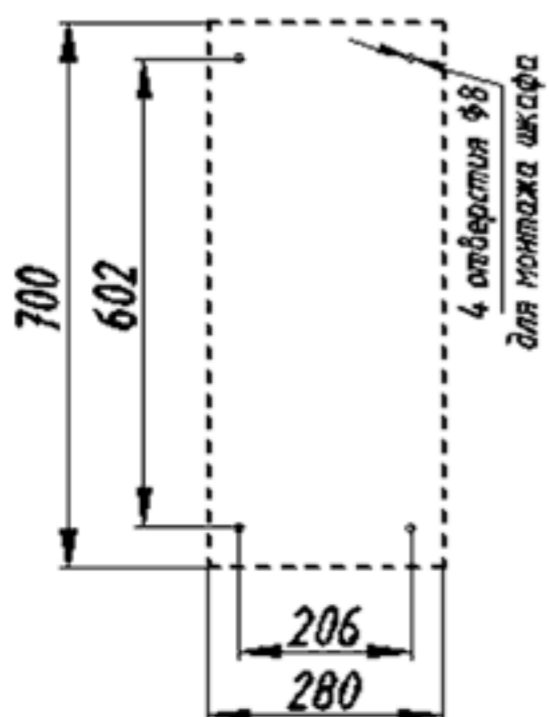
Корпус ШУ-2 навесного исполнения.
